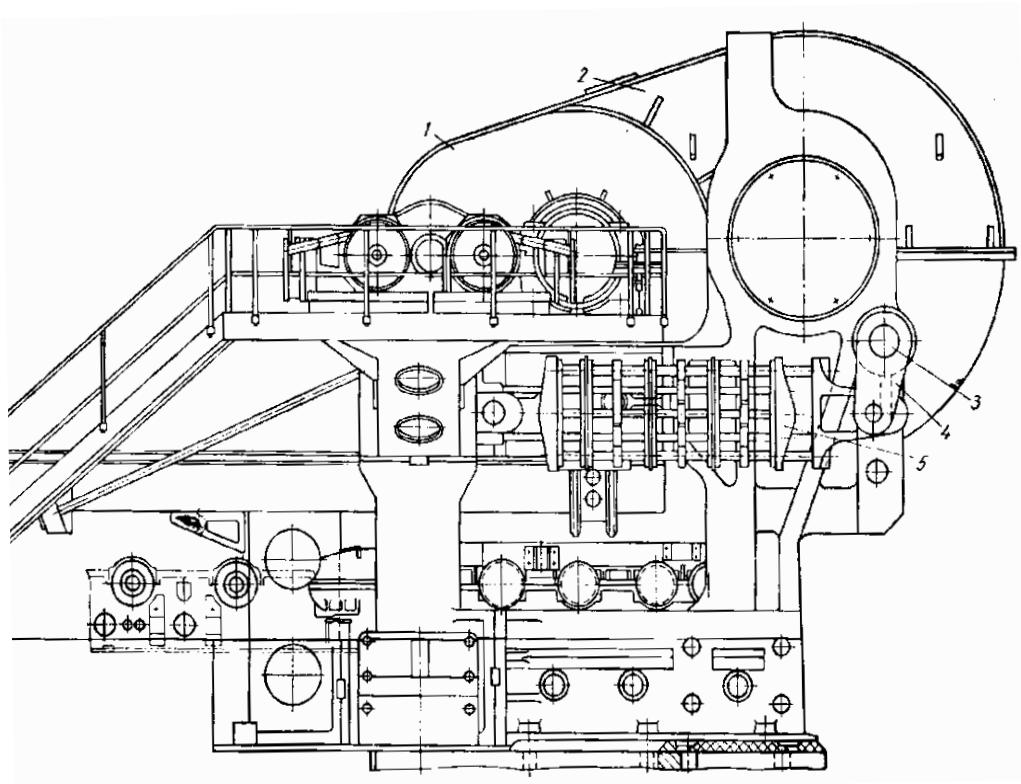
Загальний вигляд ножиць з верхнім різом
